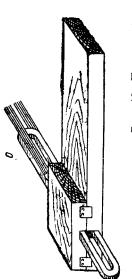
Универсальный шаблон для изготовления якорных секций: 1 — металлические щеки; 2 — упор; 3 — трубка.
